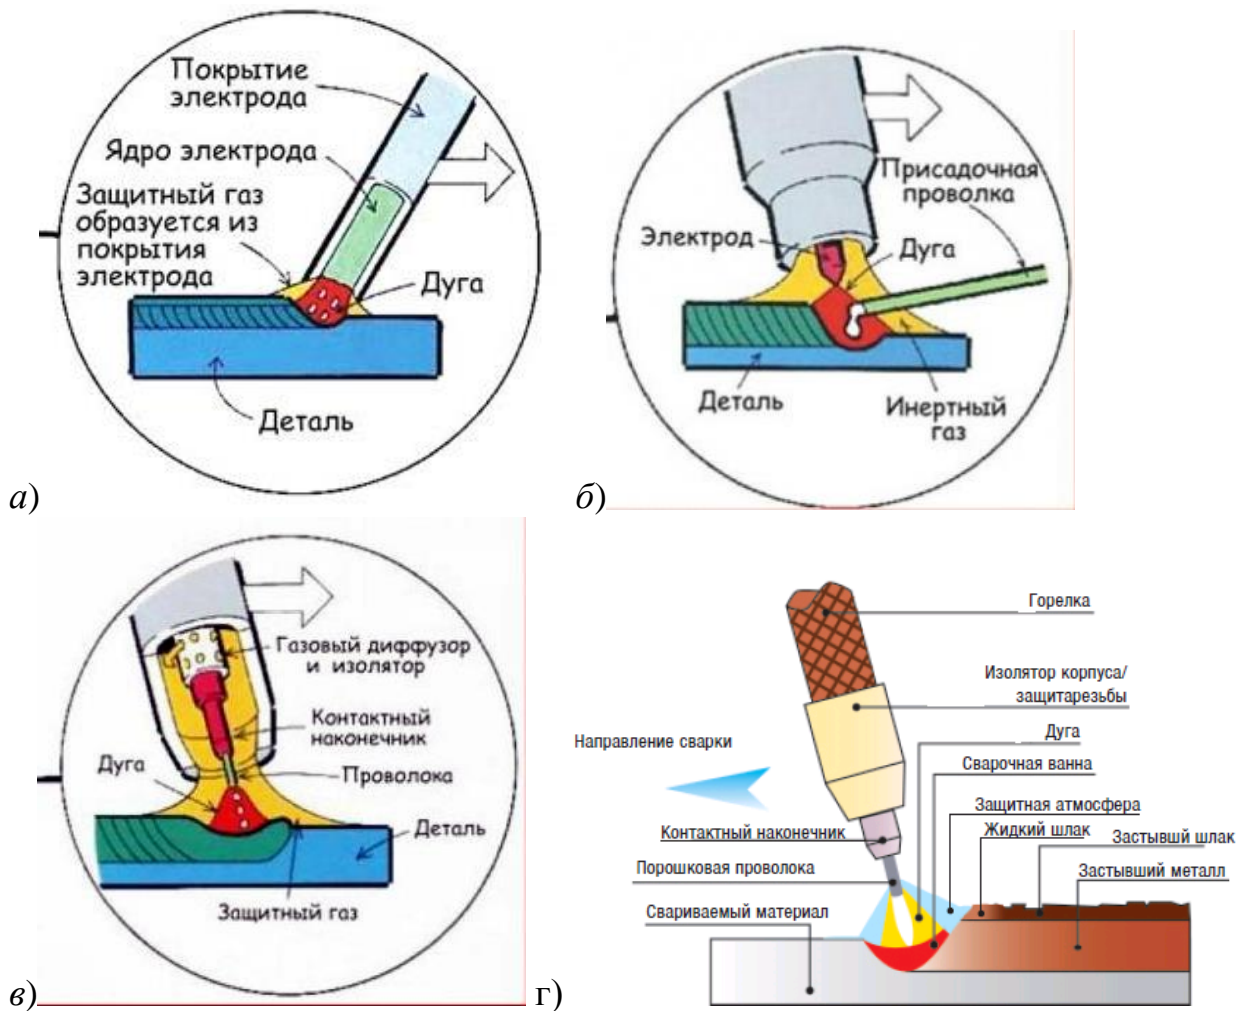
Анализ возможных способов сварки: ручная дуговая сварка (а), сварка неплавящимся электродом (б), механизированная сварка в защитном газе (в), сварка самозащитной порошковой проволокой (г)
